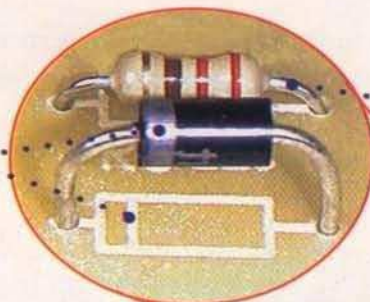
El ensamblaje de la tarjeta es muy sencillo, ponga especial cuidado al momento de soldar.
